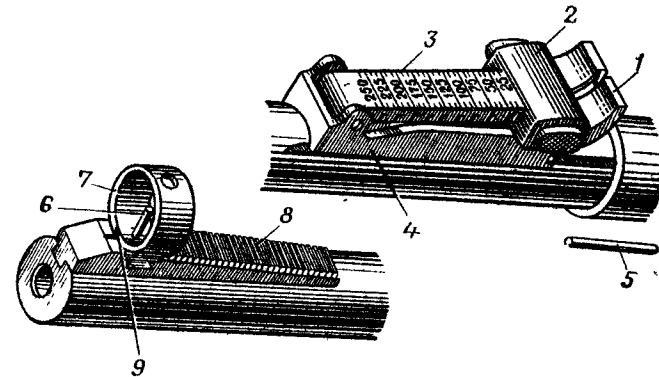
Прицельное приспособление малокалиберной винтовки ТОЗ-8:
